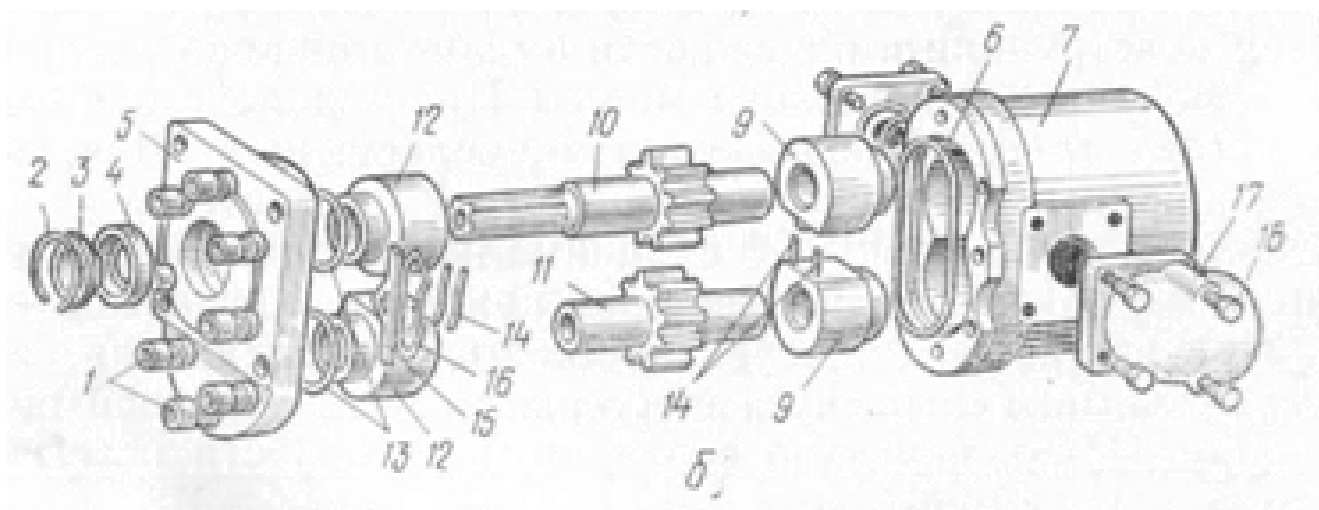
Шестеренный насос-гидромотор МНШ: 1, 18 — винты, 2, 3 — стопорное и опорное кольца уплотнения, 4 — уплотнение, 5 — крышка, 6 — уплотнительное кольцо крышки, 7 — корпус, 8 — коническое резьбовое отверстие, 9, 12 — задние и передние втулки, 10, 11 — ведущий и ведомый валы-шестерни, 13— уплотнительные кольца передних втулок, 14—направляющие проволоки, 15 — разгрузочные пластины, 16 — уплотнительные кольца, 17 — патрубок.
